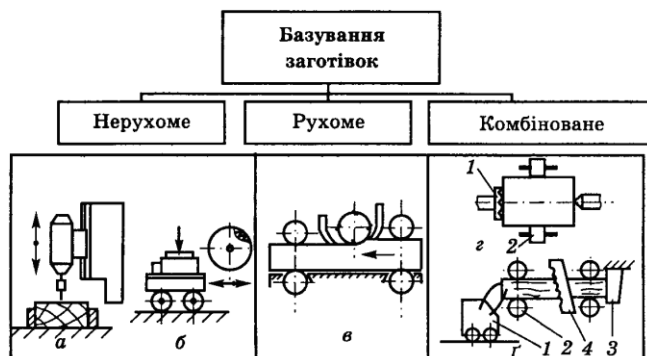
Способи базування заготовок: а, б – нерухоме; в – рухоме; з – комбіноване: 1 – кулачки шпинделя; 2 – люнет; г – комбіноване: 1 – візок; 2 – подавальні вальці; 3 – напрямні ножі; 4 – пила
